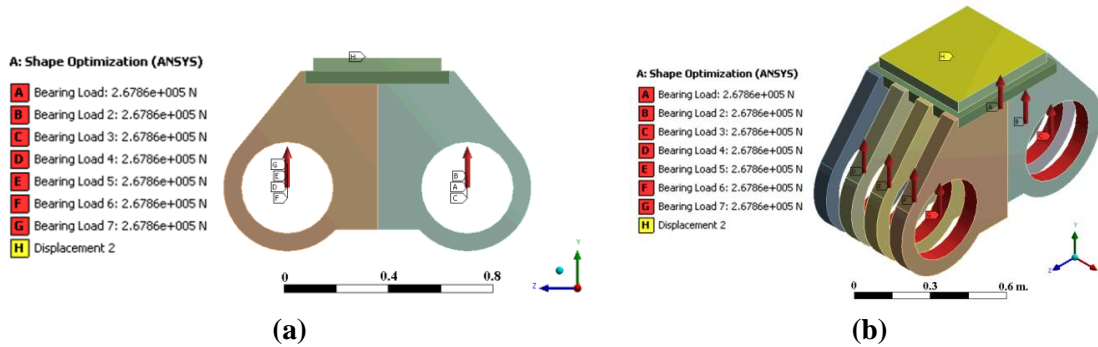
Cargas aplicadas: (a) vista frontal; (b) perspectiva isométrica.
